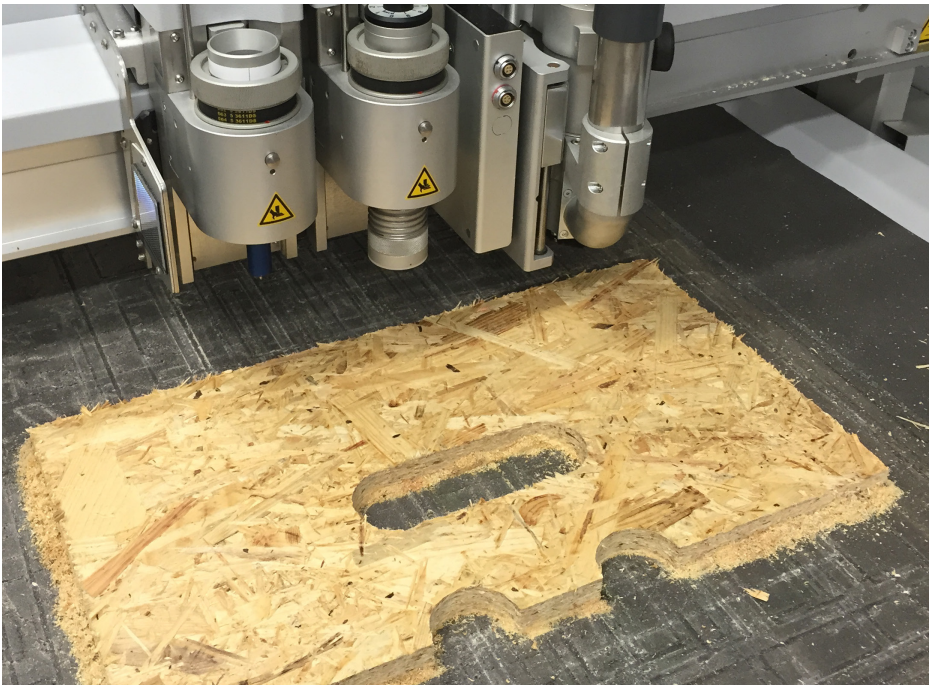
Fräsarbeiten auf einer ZÜND-CNC Fräse
